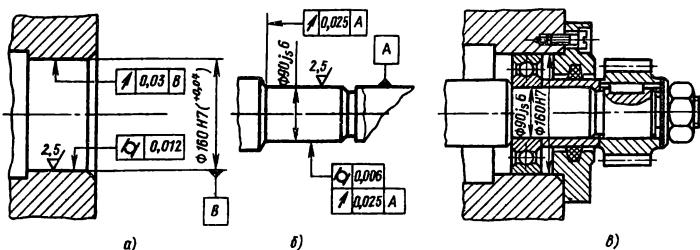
Обозначение допусков и посадок подшипника качения:
